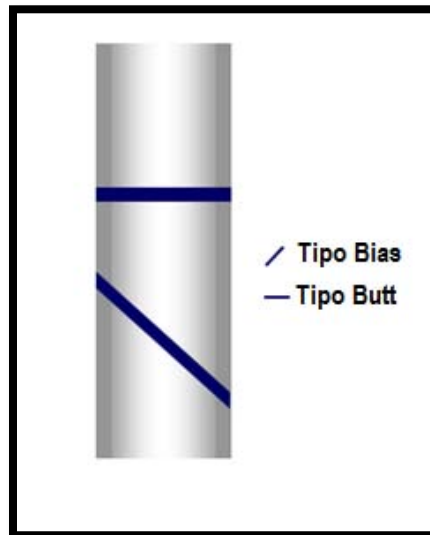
3. Tipos de soldaduras para la tubería flexible.
